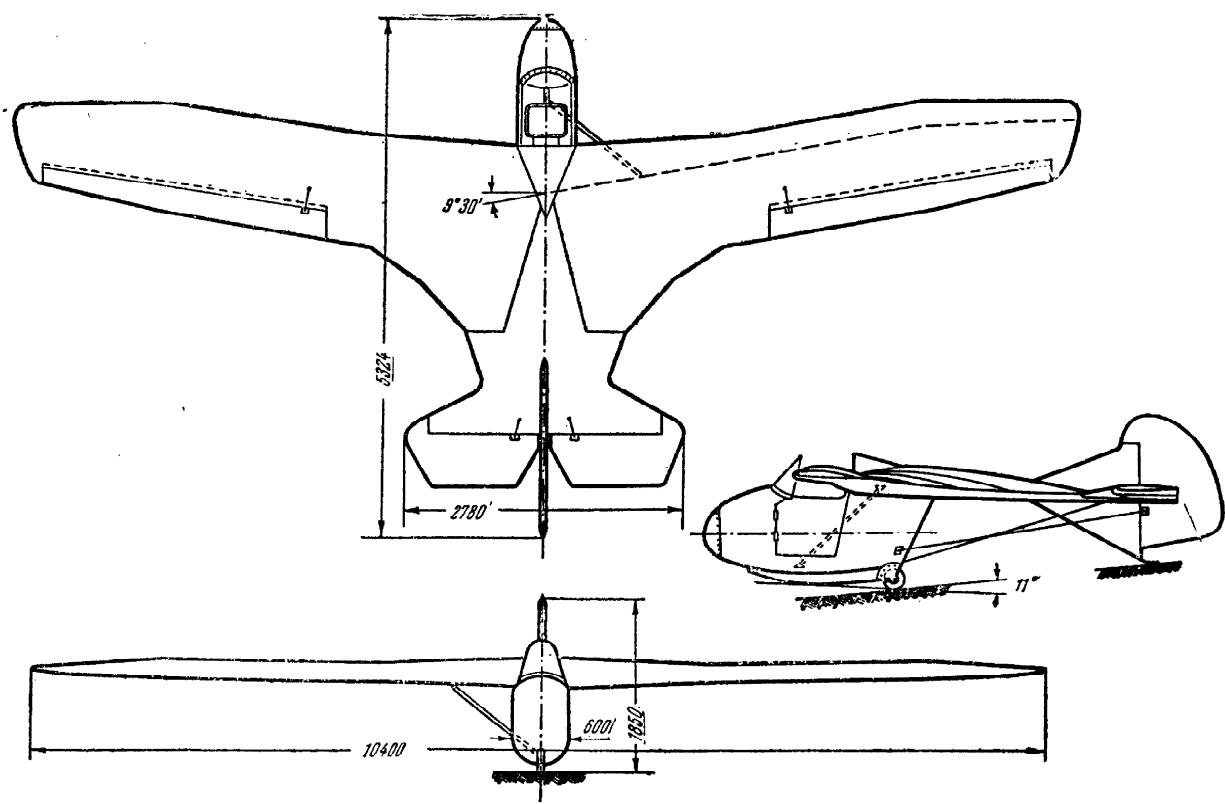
Схема планера MAK-15 конструкции М. А. Кузакова
